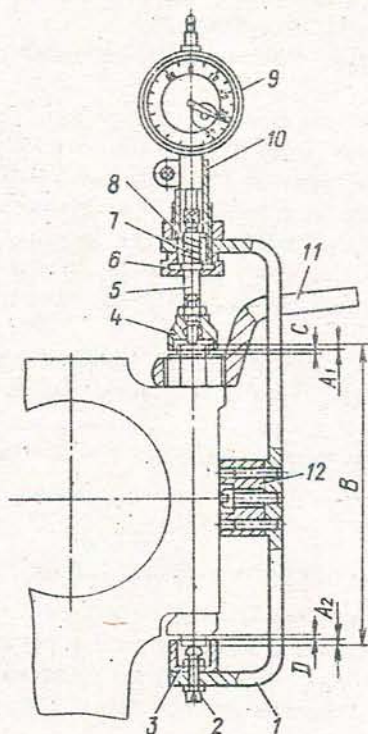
Приспособление для замера удлинения шатунных болтов при затяжке:
